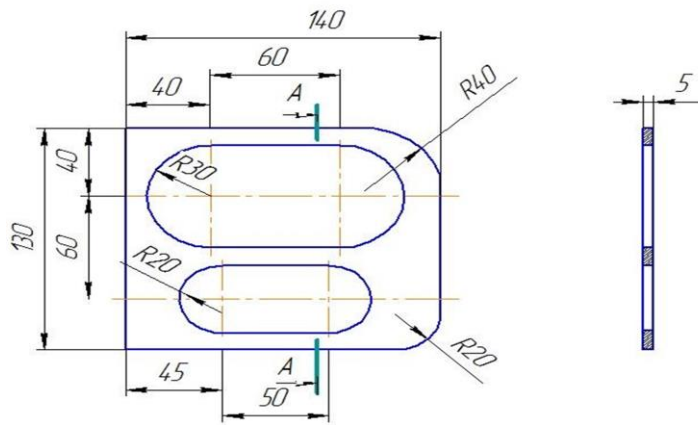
Эскиз 1 образца с различным сочетанием поверхностей
